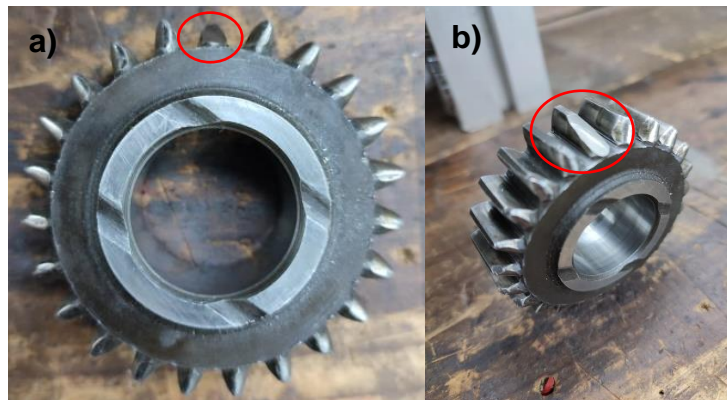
Fractura de diente en engrane (a) toma frontal y (b) toma isométrica.
